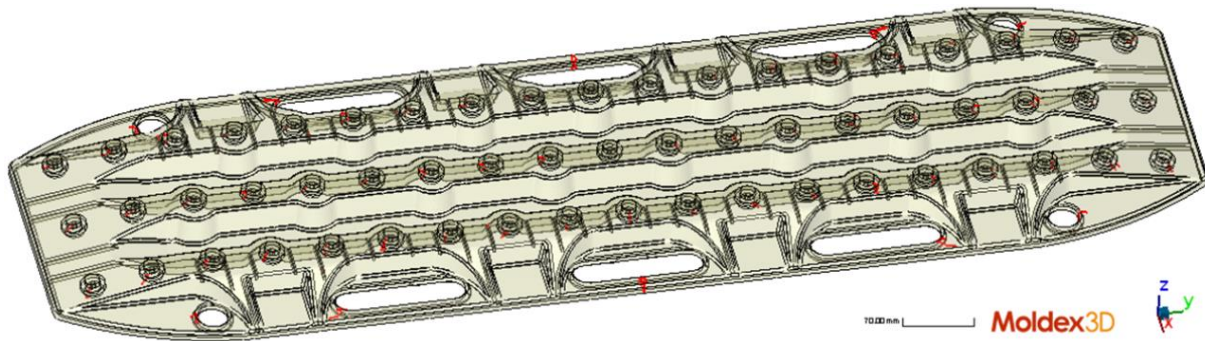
Previsão da localização de linhas de soldadura [70].
